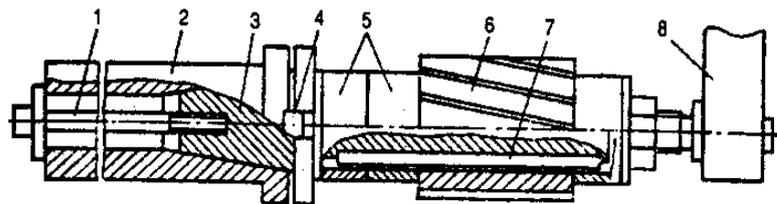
Установка цилиндрической фрезы на длинной оправке.
